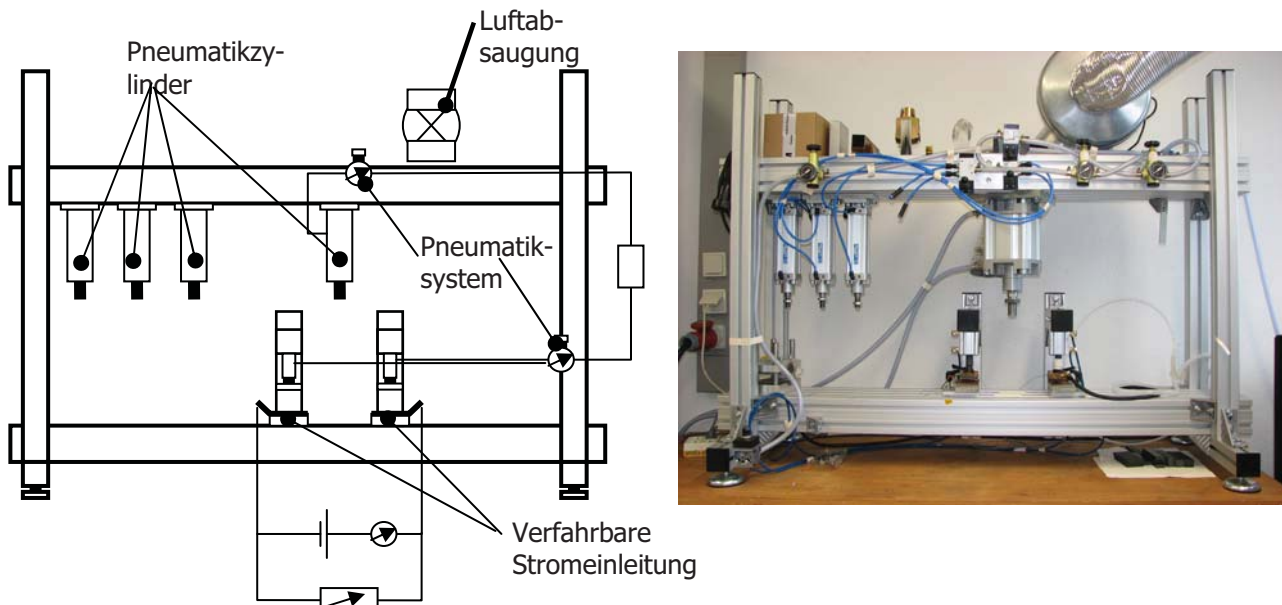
Schematische Darstellung der Proben-Schweißvorrichtung
